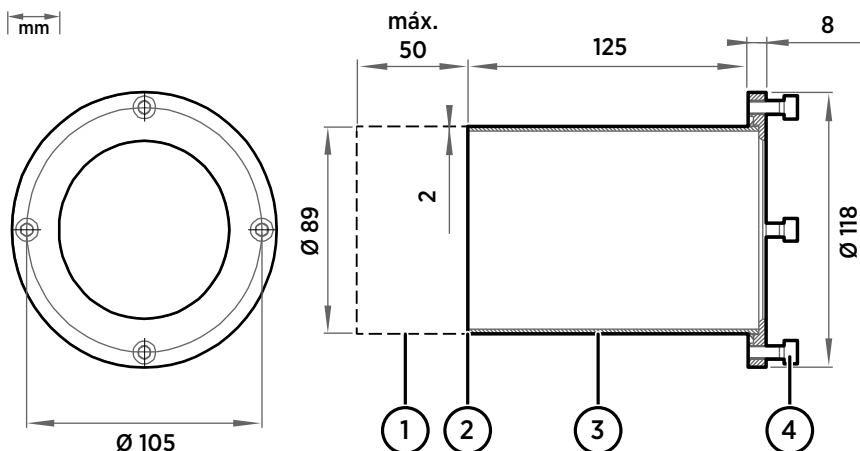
Flange de montagem do conjunto de resfriamento DMP246CS
